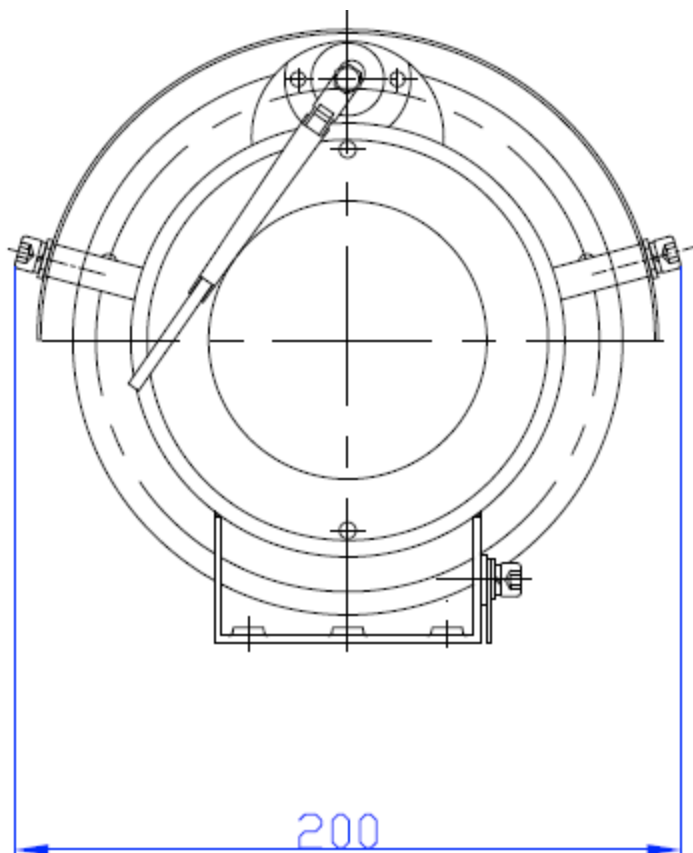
Габаритные размеры TKNCL-9, вид спереди
